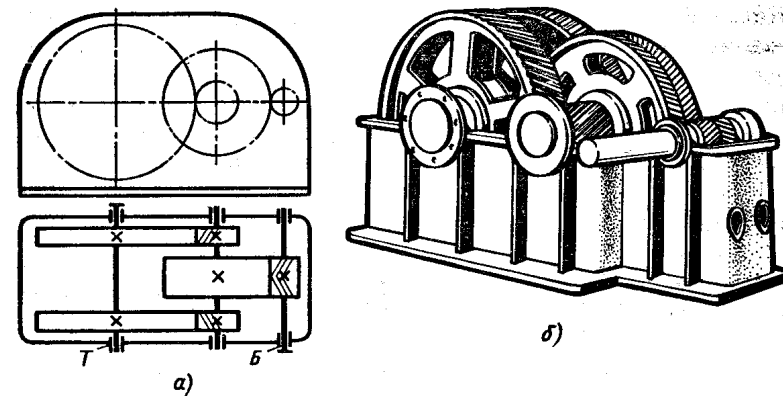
Двухступенчатый горизонтальный редуктор с раздвоенной второй (тихоходной) ступенью: а – кинематическая схема; б – общий вид (без крышки)
